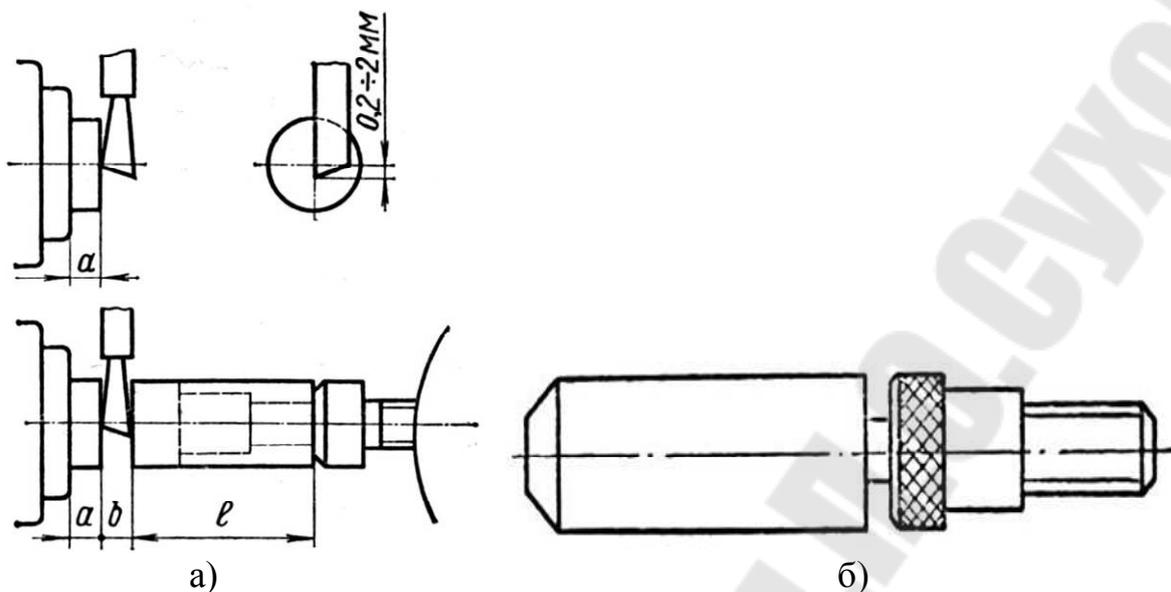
Схемы установки и регулировки отрезного резца (а), эскиз эталона для наладки инструмента (б)
